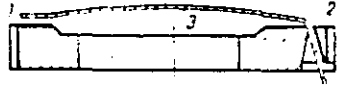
Sección del rócalo de calita para un interruptor eléctrico con contactos metalizados (1,2) y soldadura por inmersión del resorte 3
